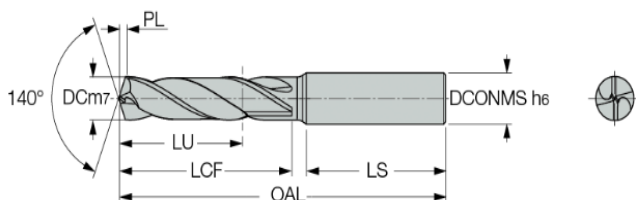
Загальний вигляд свердла DSM 180-054-25A-3D
